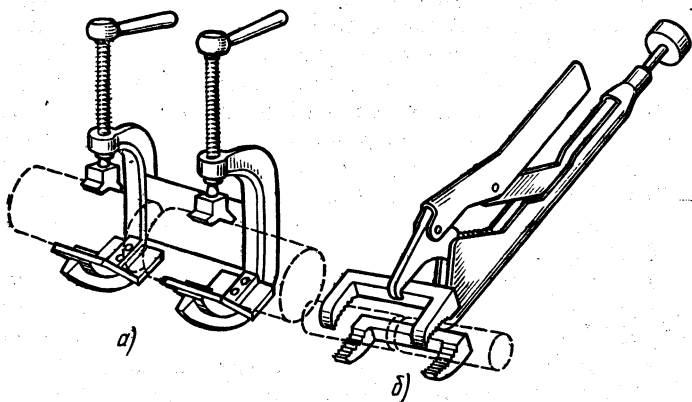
Приспособление для центровки труб (*a*) и клещи СТД-997 (*б*)
